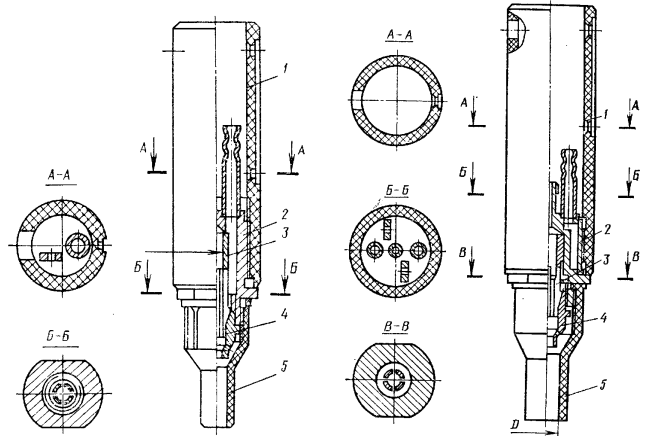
Сварочная горелка типа 2ГНА-160:
